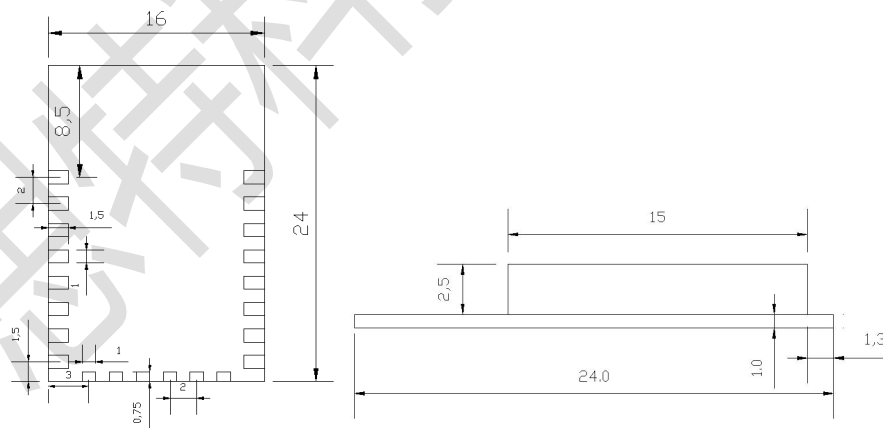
FST66\_04D 模组尺寸平面图 (单位: mm)
